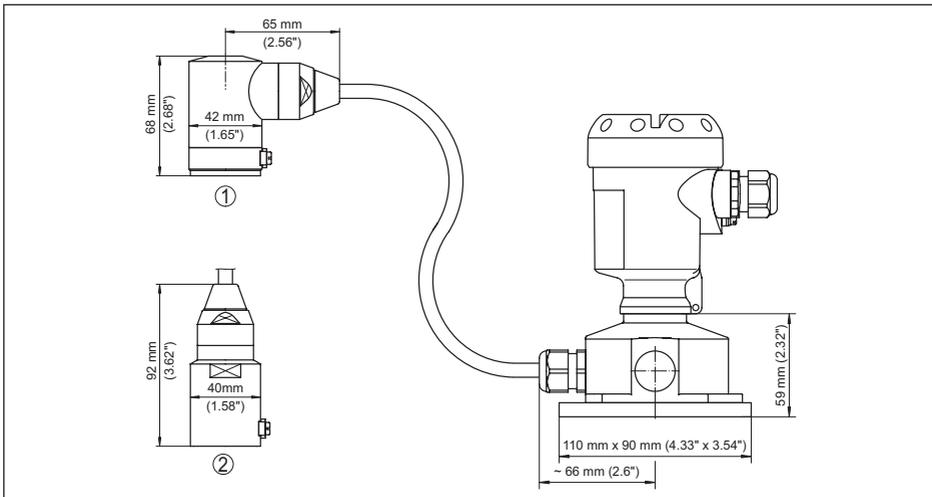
IP 68-Ausführung mit externem Gehäuse
